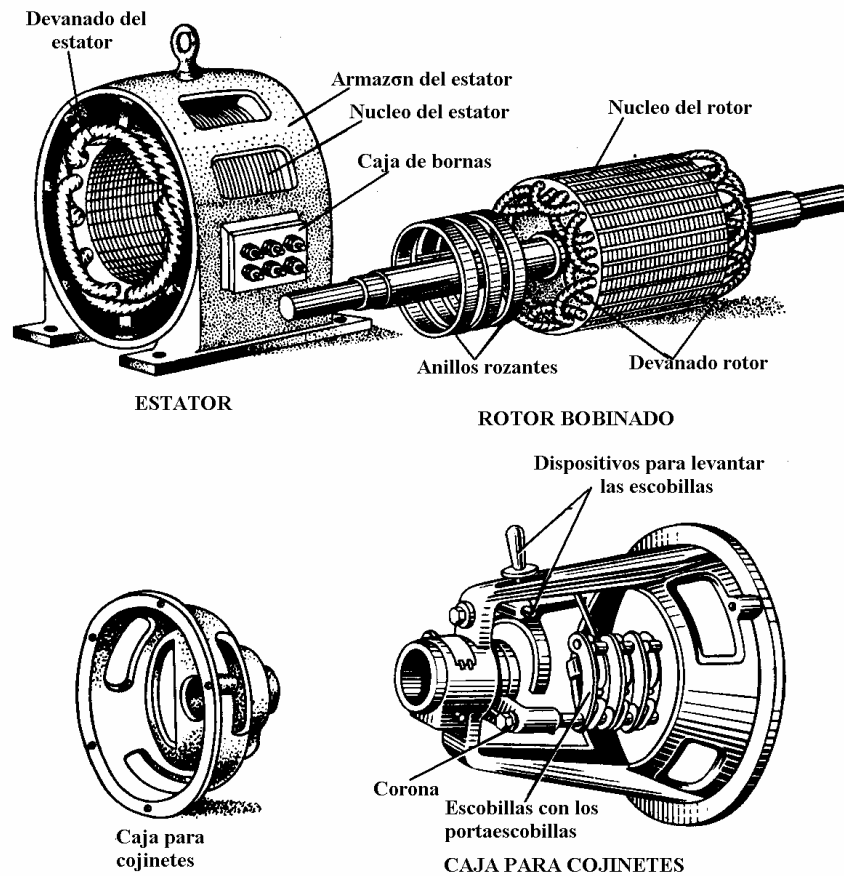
Motor asíncrono con rotor bobinado. Secciones y detalles de su forma constructiva.
